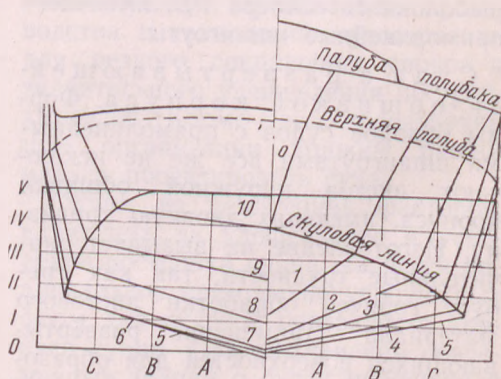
Теоретический чертеж сейнера РБ с развешивающимися поверхностями обшивки корпуса.
